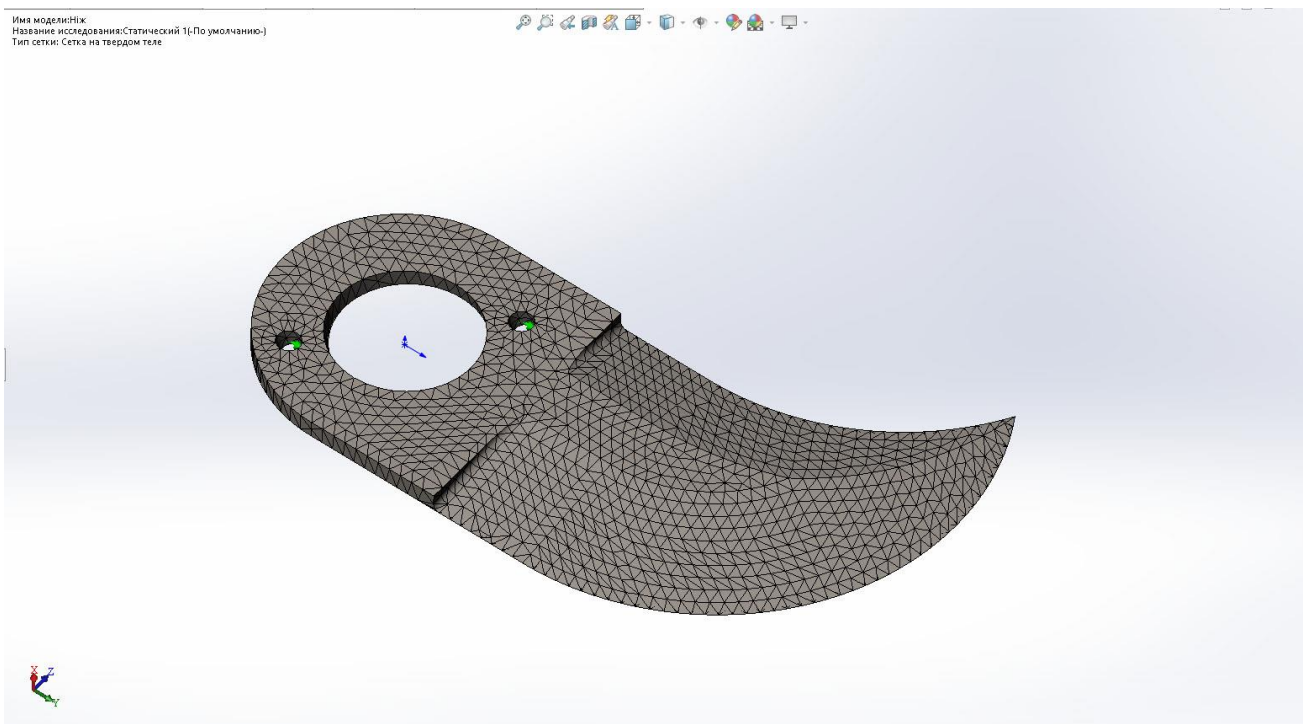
Розрахункова сітка ножа з двома сформованими кромками
